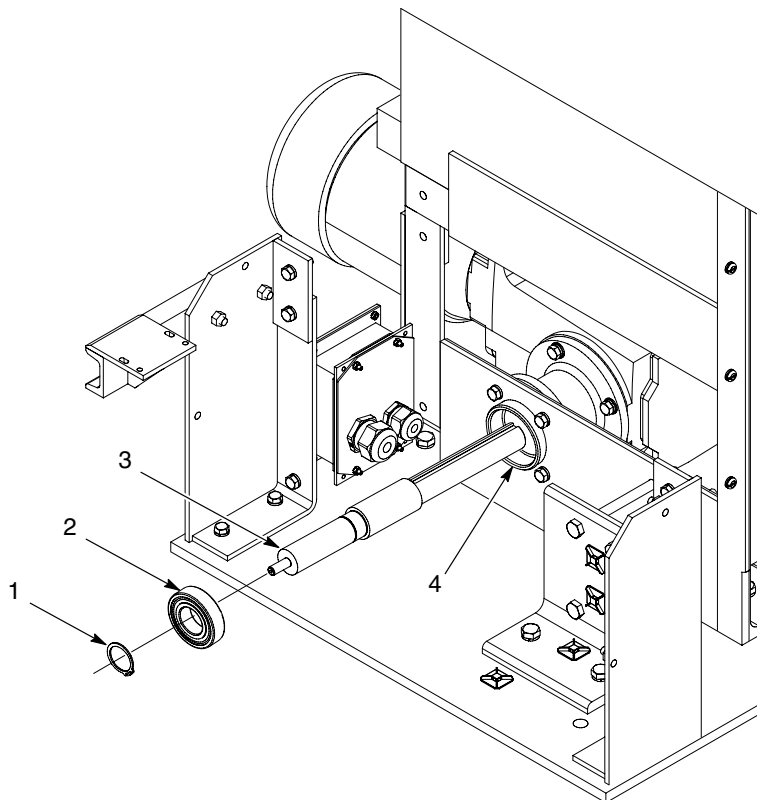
Lager oder Getriebemotorwelle ersetzen
